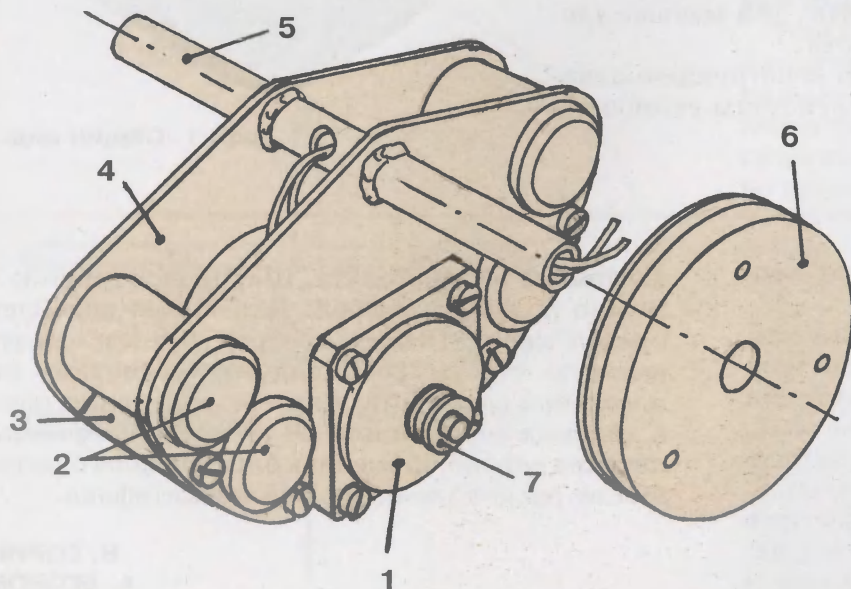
Общий вид моторного отсека: 1 — электродвигатель; 2 — батареи питания; 3 — втулка свинцовая; 4 — рама; 5 — ось; 6 — большой шкив; 7 — малый (ведущий) шкив.
